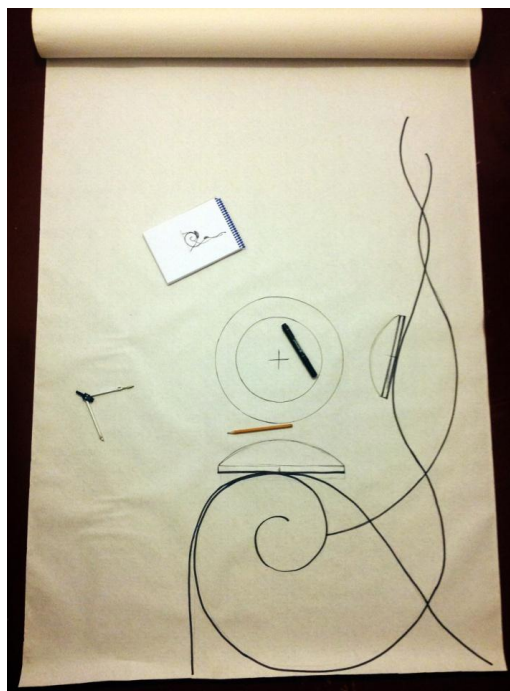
Изготовление ориентировочного трафарета для изготовления деталей конструкции.
